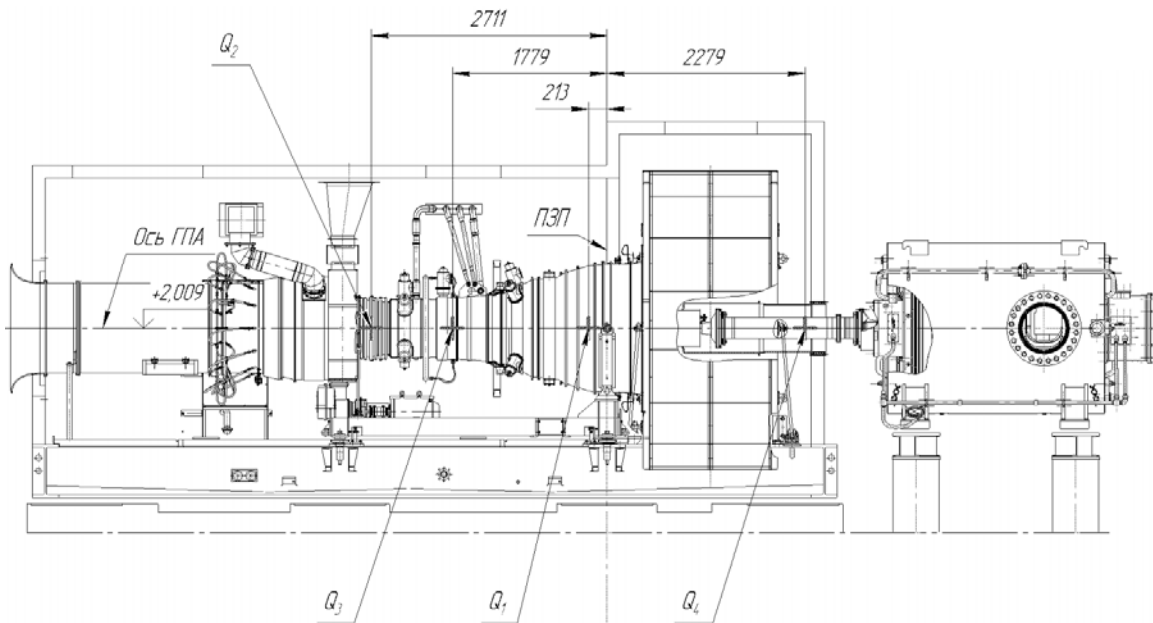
Схема расположения центров вращающихся частей двигателя
